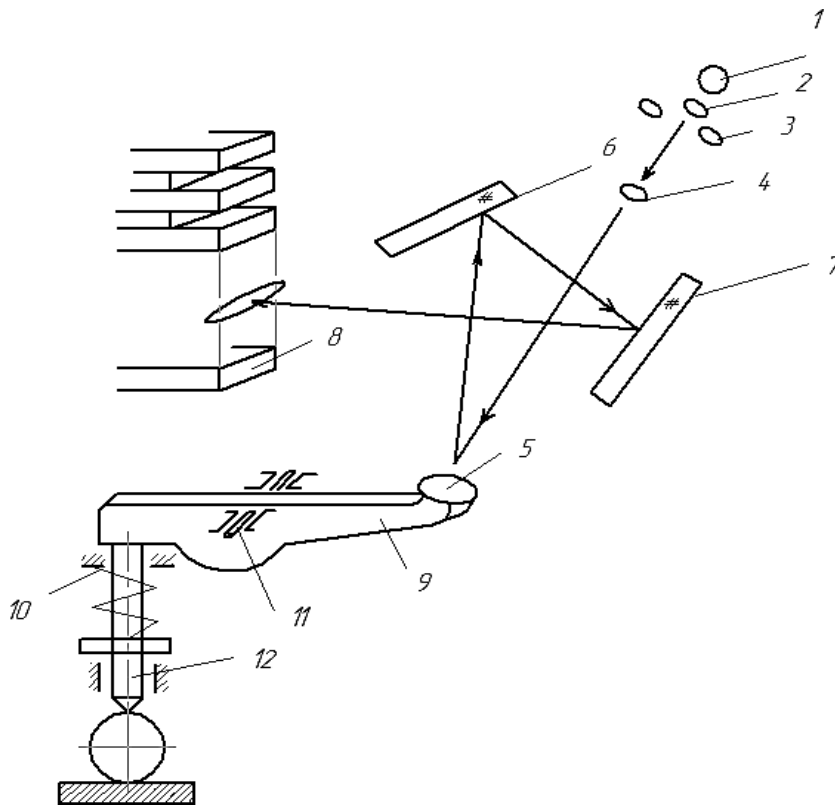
Фотоелектричний вимірювальний пристрій
